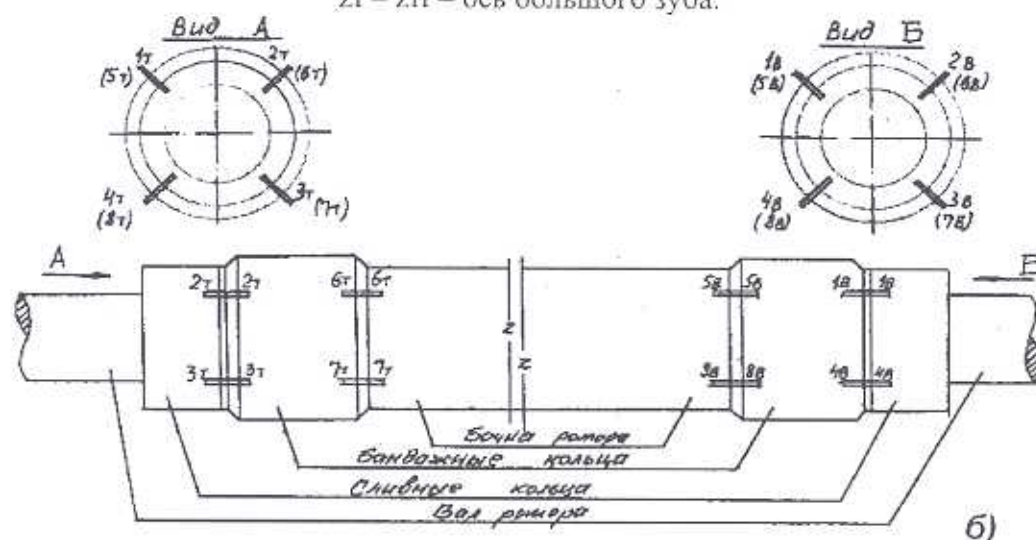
б) Схема маркировки узлов и деталей ротора.
